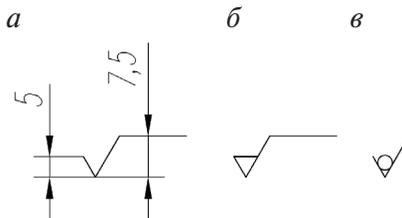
Знаки для обозначения шероховатости поверхности
